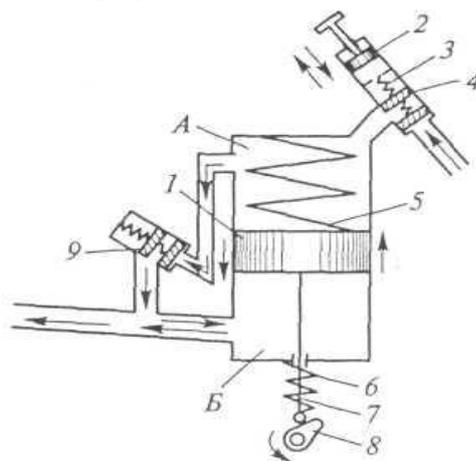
Схема топливopодкачивающего и ручного насосов: 1,2 - поршни; 3,5, 6 - пружины; 4,9 - клапаны; 7 - шток; 8 - эксцентрик; А, Б – полости.
